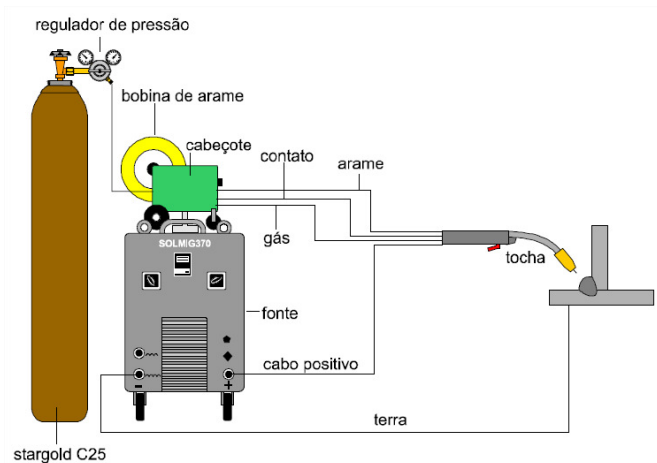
Ilustração equipamento soldagem MIG / MAG.
